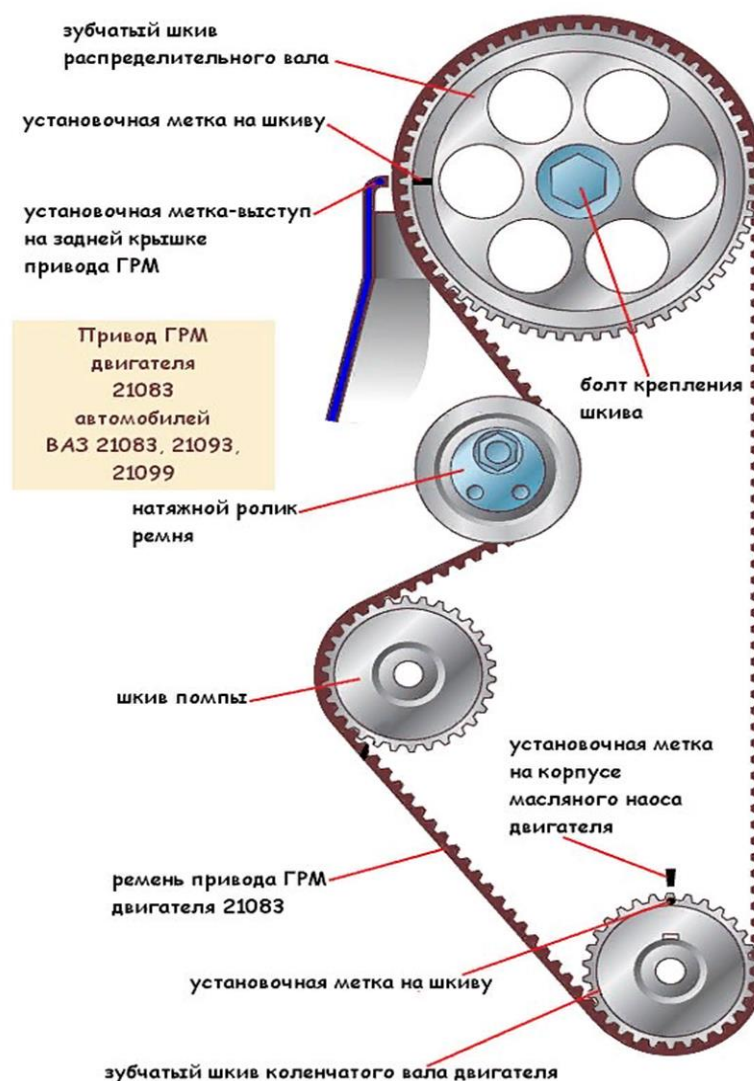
Привод ГРМ двигателя ВАЗ 21083
